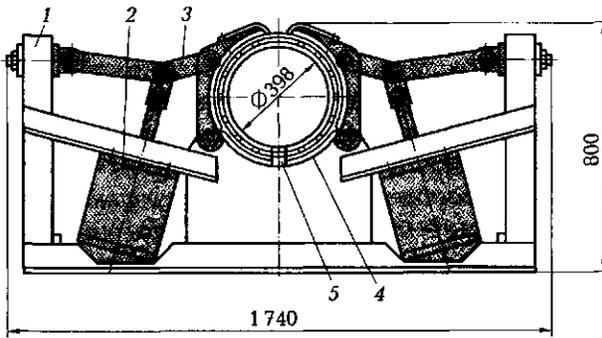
Приспособление для сборки продольных стыков обечаек малого диаметра:
